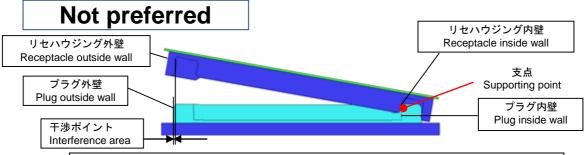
外壁合わせによる嵌合 Fig.2 Diagonal mating by aligning Plug outside wall
